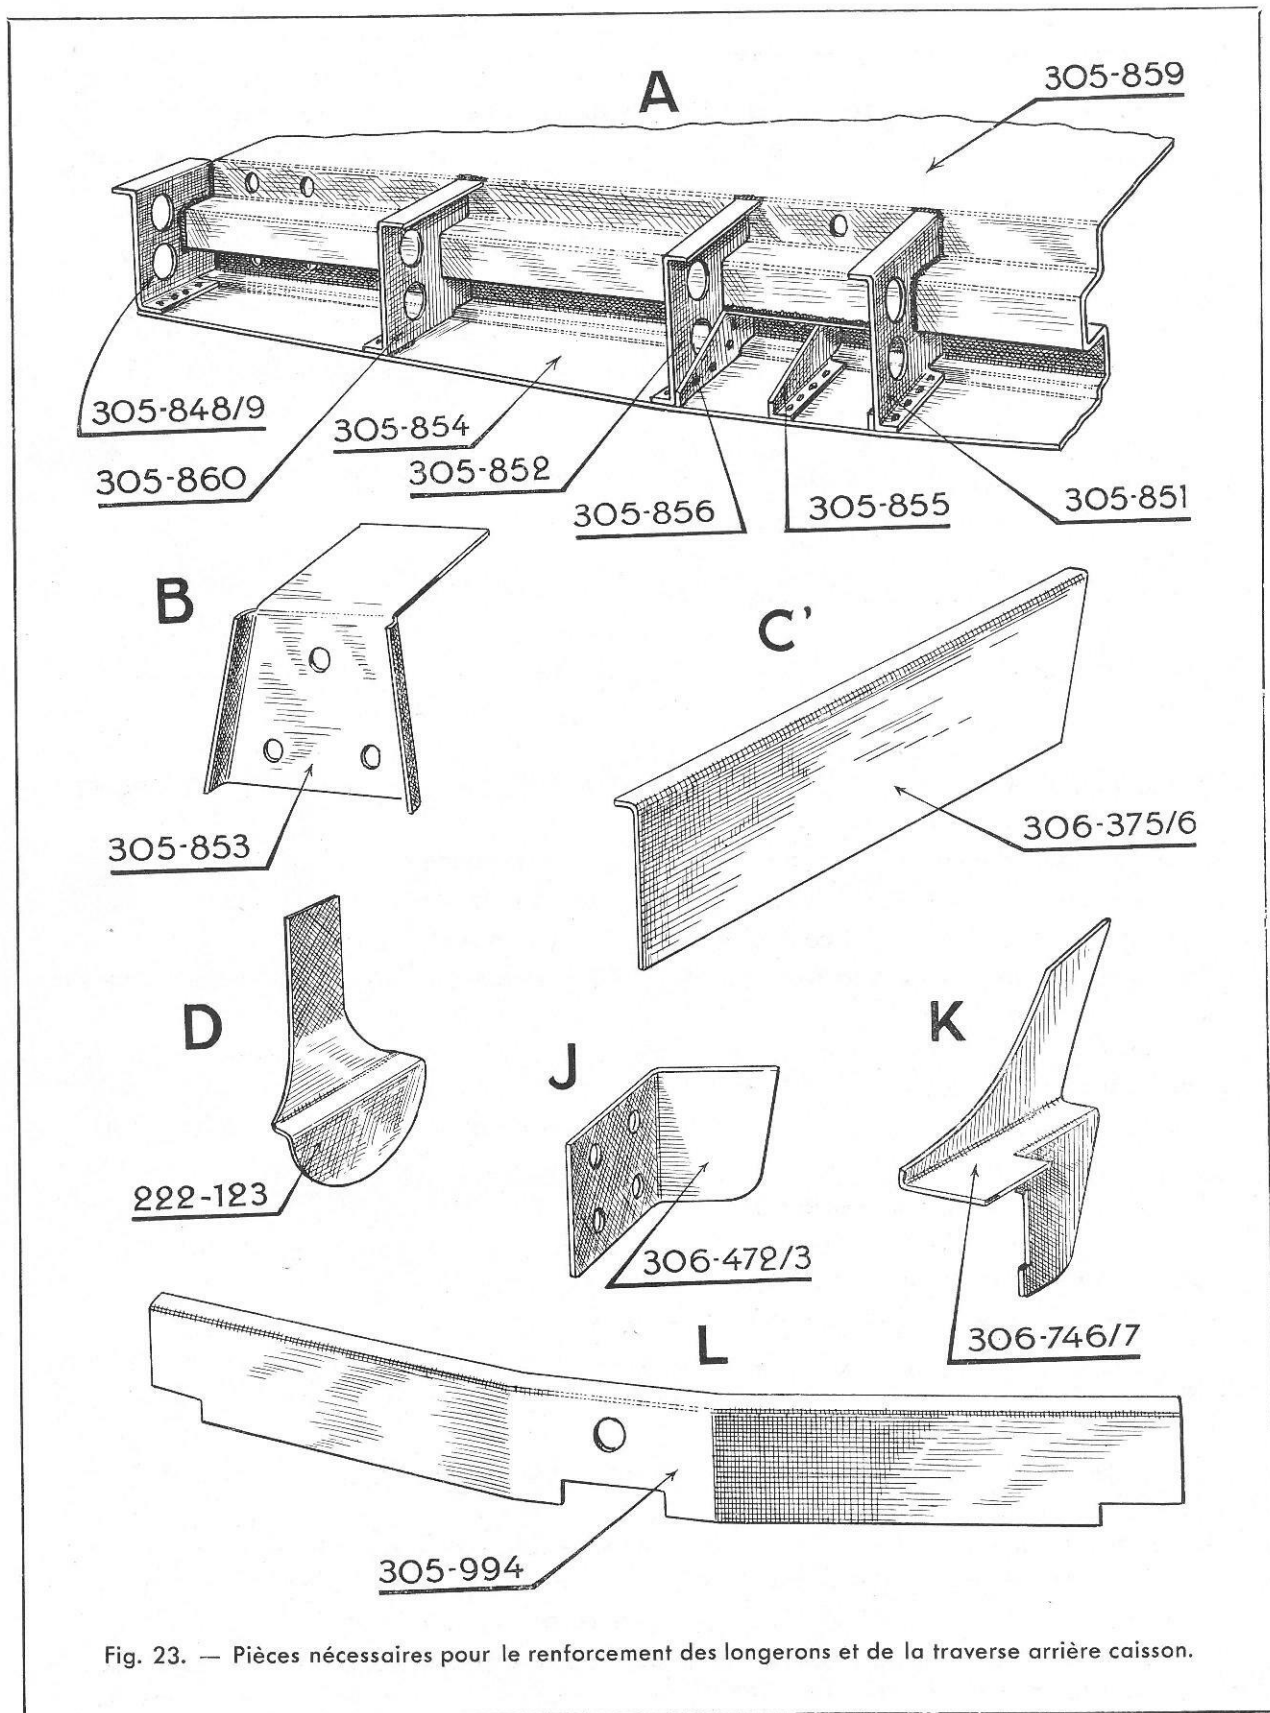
Pièces nécessaires pour le renforcement des longerons et de la traverse arrière caisson.
